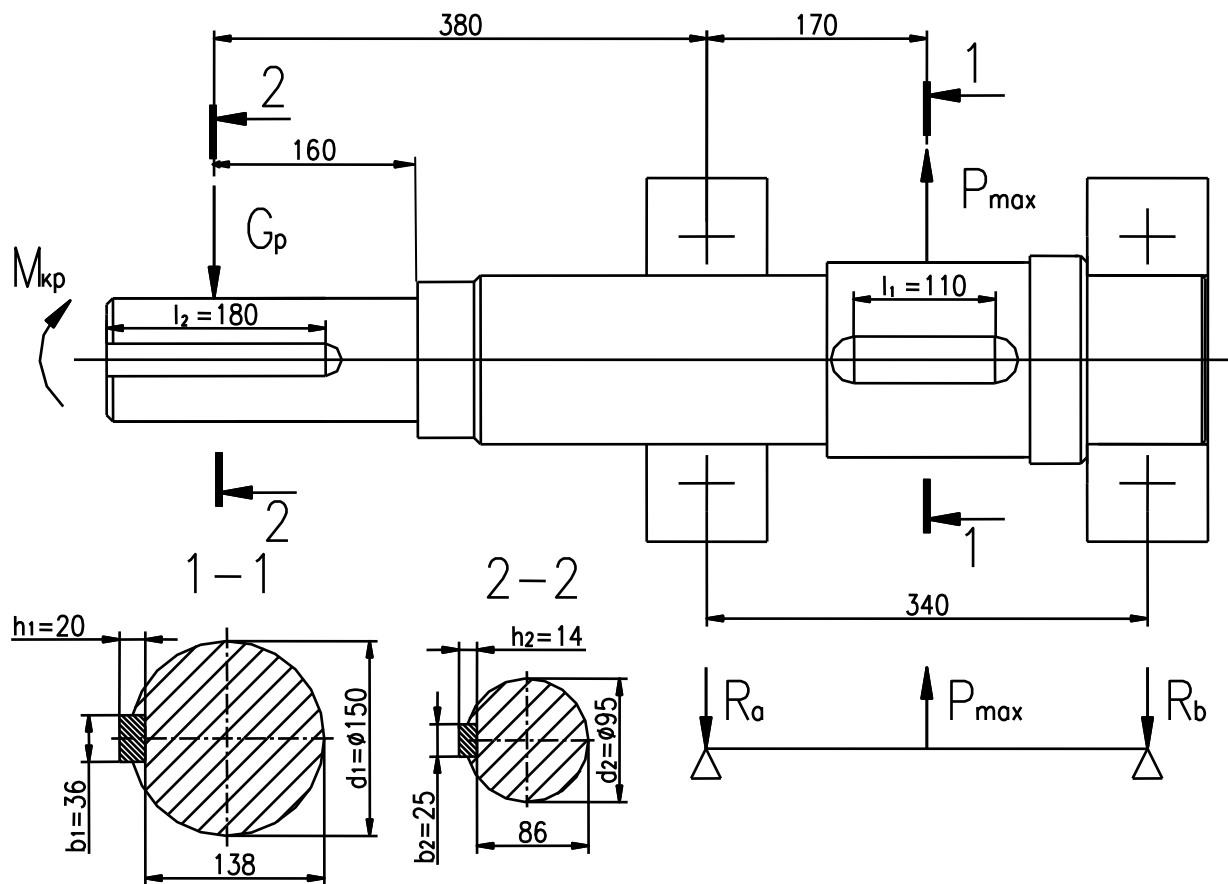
Розрахункова схема вала привідного колеса
